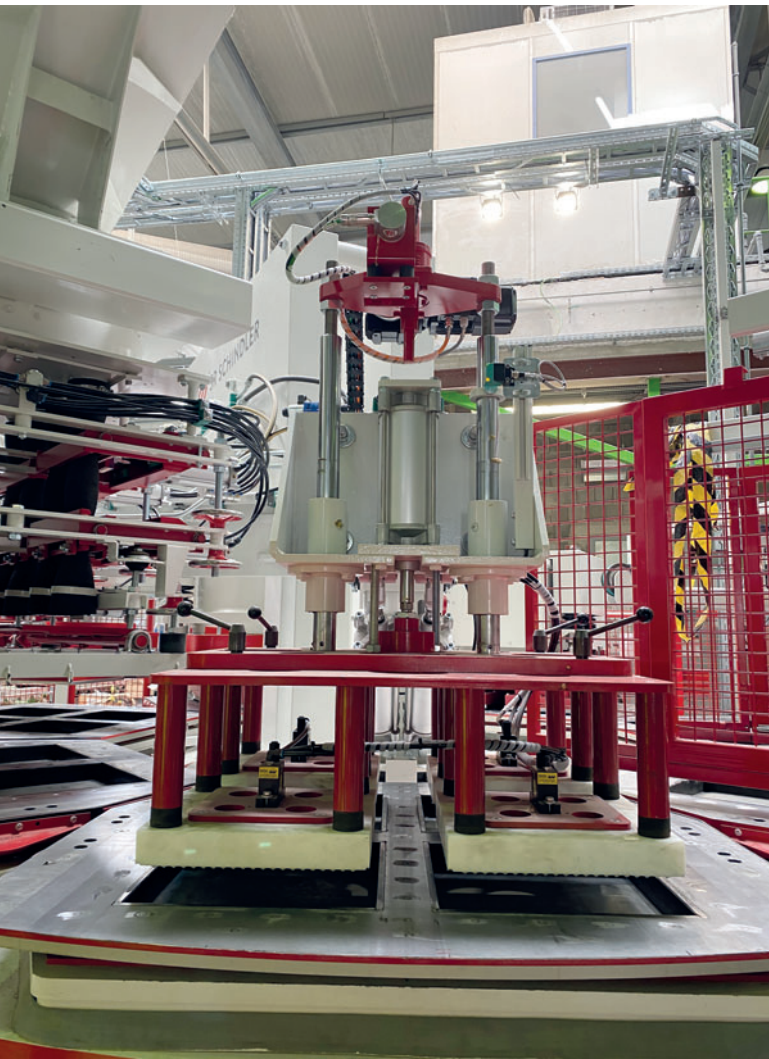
Doseur à tuyau flexible à gauche sur la photo et distributeur de béton de parement au premier plan
